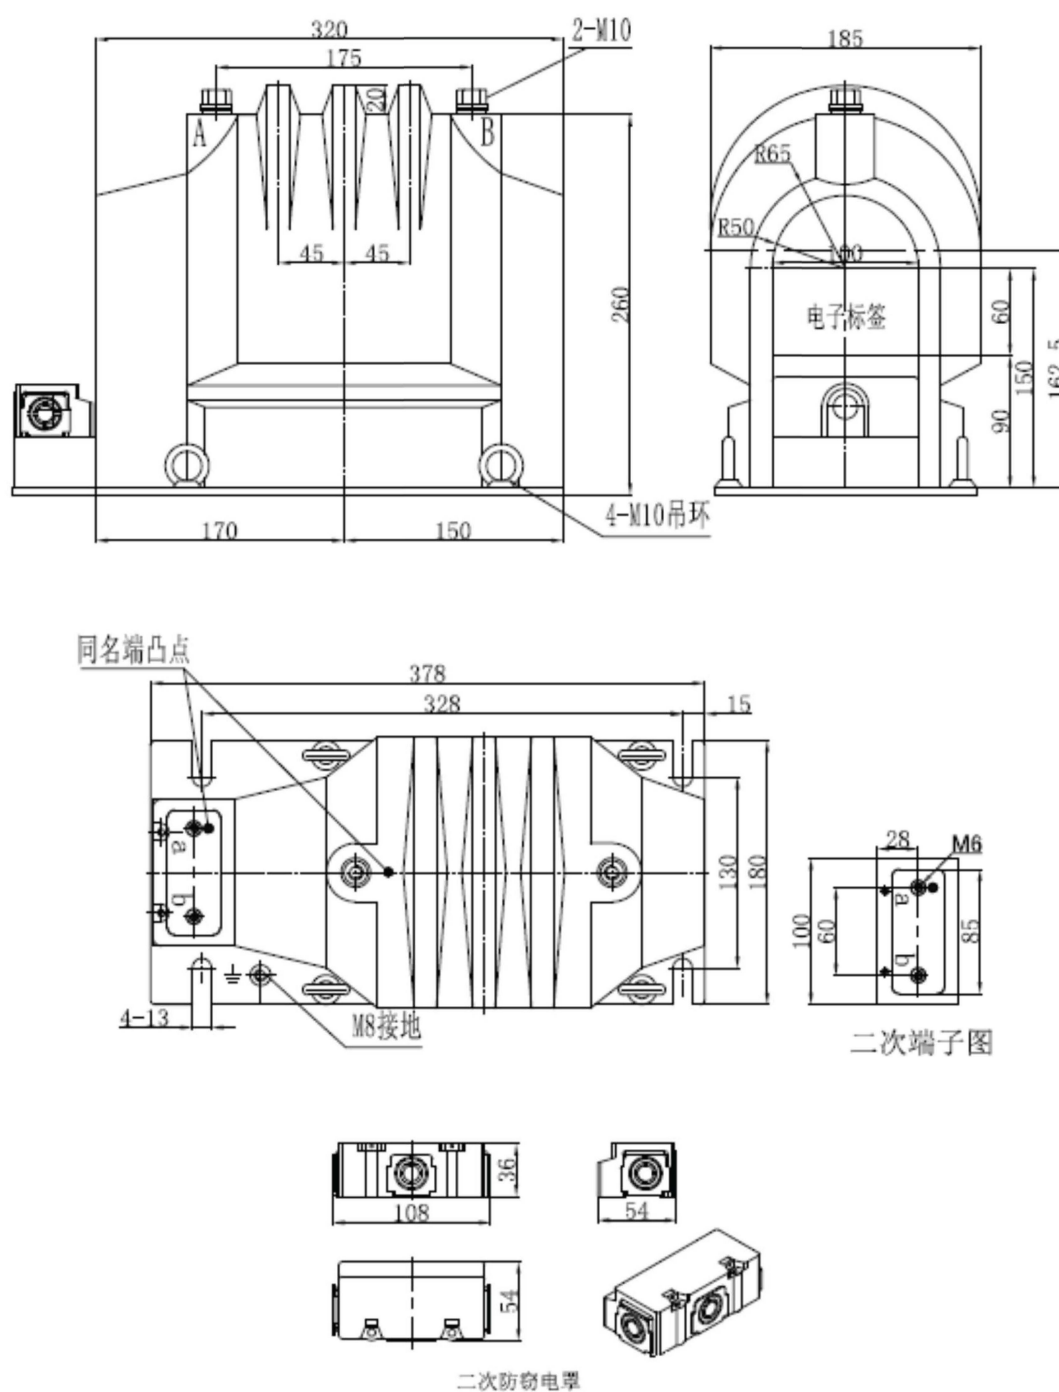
JDZQN-10型不接地式电压互感器外形尺寸 (mm)
